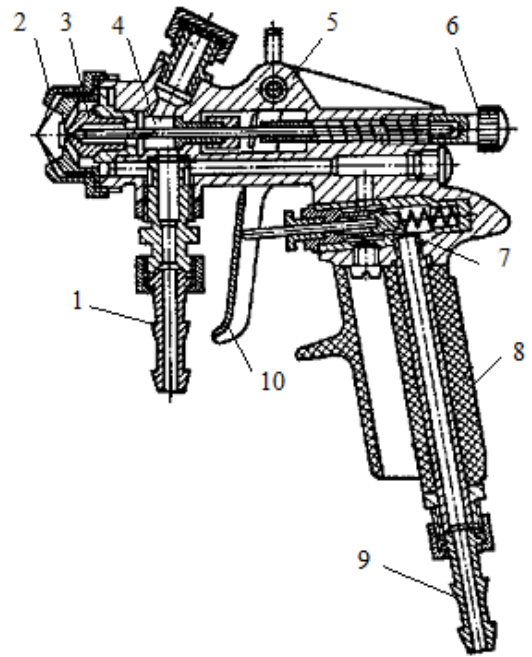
Пневматический краскораспылитель с универсальной головкой: 1 – штуцер; 2 – головка распылительная; 3 – сопло; 4 – игла; 5 – корпус; 6 – регулятор; 7 – воздушный клапан; 8 – рукоятка; 9 – штуцер; 10 – нажимная скоба
